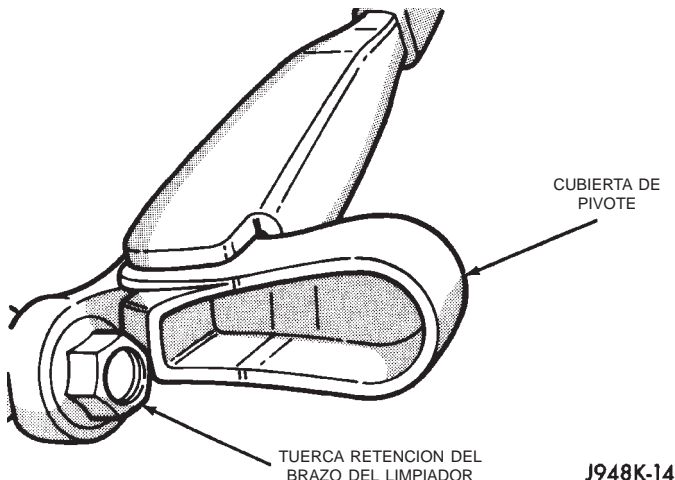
Desmontaje e instalación de brazo de limpiador trasero
